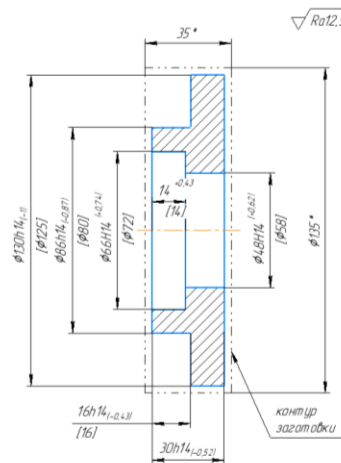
Ескіз основи під адитивне наплавлення заготовки
